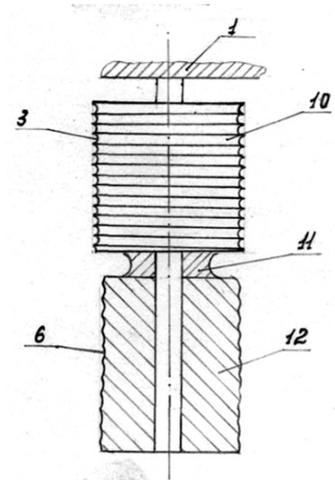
Устройства для изготовления заготовок приводных ремней (вариант 2)
